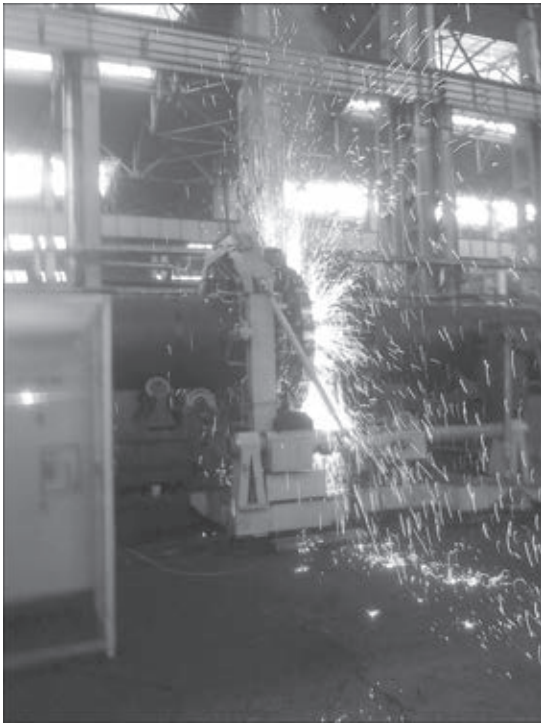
Комплекс для контактной стыковой сварки оплавлением морских трубопроводов диаметром 1219 мм с толщиной стенки 27 мм
